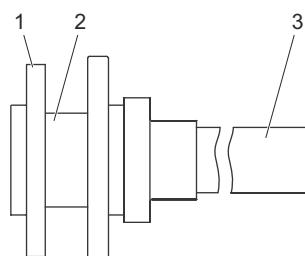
Стандартный инжекционный клапан до 4000 л/ч
